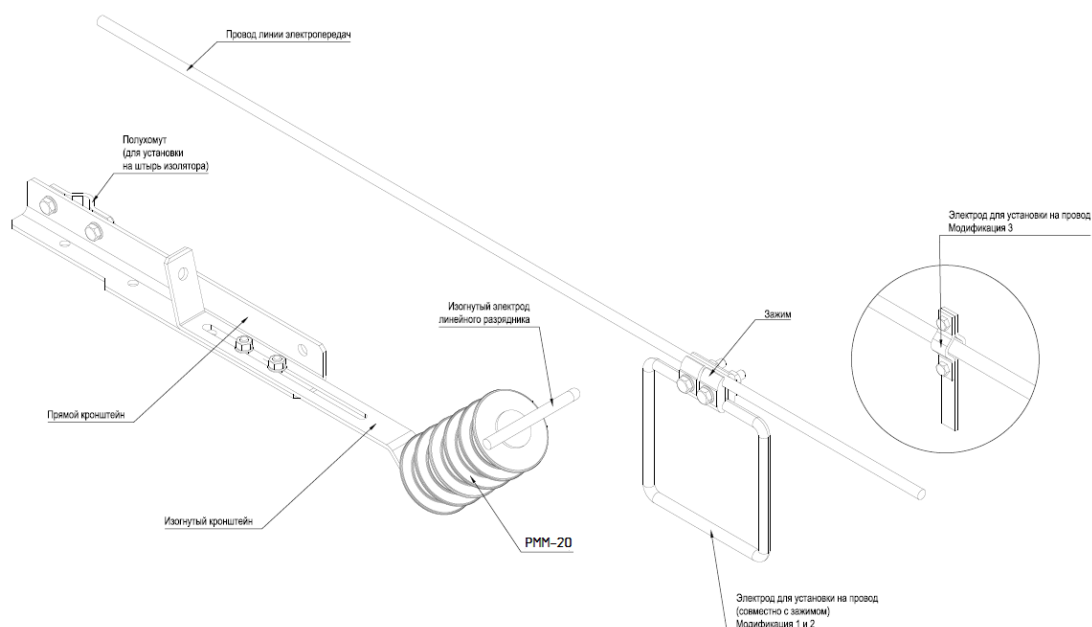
Комплект деталей для установки устройства РММ-20 на промежуточной опоре со штыревыми изоляторами.
